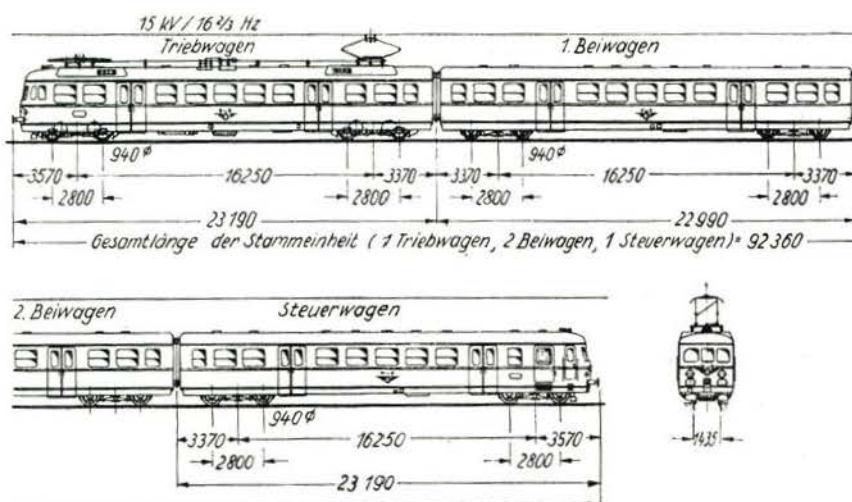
Maßskizze der Reihe 4030 (Skizze: H. Köhler)
